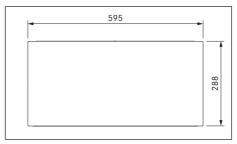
Dimensiones del aparato vista frontal MSS290
